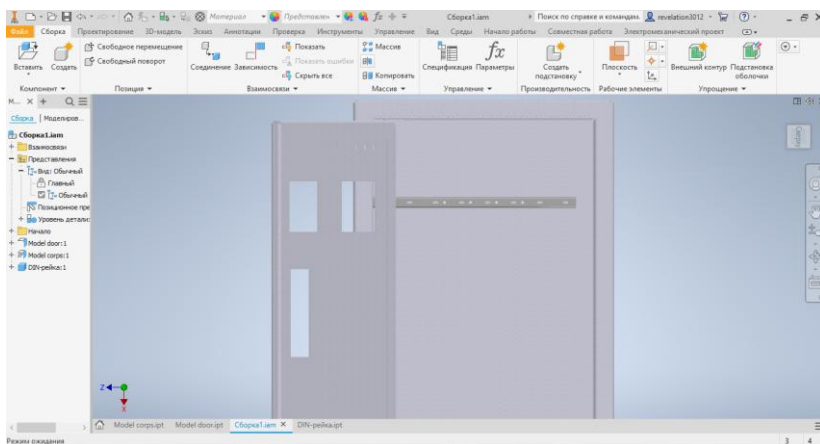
Вигляд закріпленої DIN-рейки на корпусі
